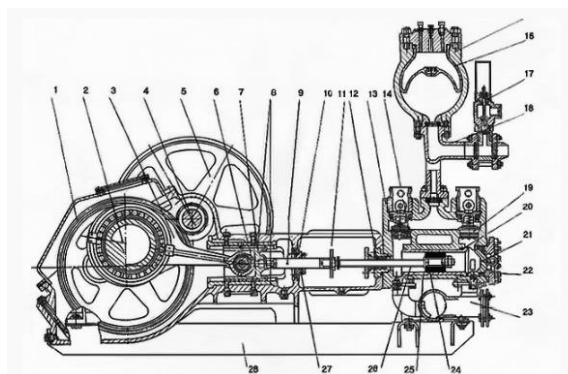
Основные детали насоса буровой установки: 1-косазубая передача, 2-эксцентриковый вал, 3-шатун, 4-трансмиссионный вал, 5-шкив, 6-головка шатуна, 7-пологун, 8-накладки, 9-шток, 10-корпус сальника, 11-диск-отражатель, 12-уплотнение штока поршня, 13-гидравлическая коробка, 14-седло клапана, 15-компенсатор, 16-диафрагма, 17-клапан предохранителей, 18-нагнетательный коллектор, 19-клапан рабочий, 20-уплотнение, 21-коронка, 22-крышка цилиндра, 23-всасывающий коллектор, 24-поршень, 25-цилиндрическая втулка, 26-шток поршня, 27-уплотнение, 28-рама
